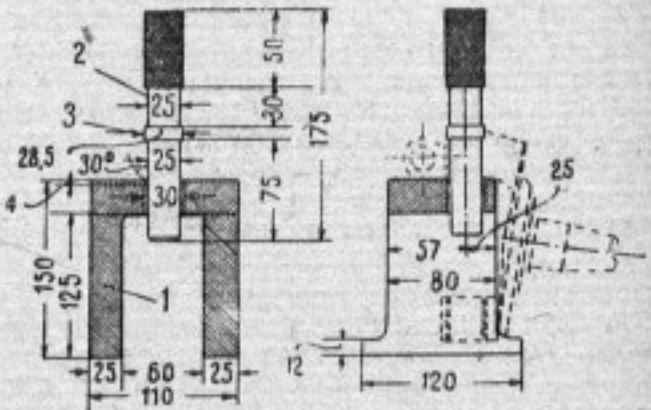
Приспособление для выпрессовки и запрессовки втулок
